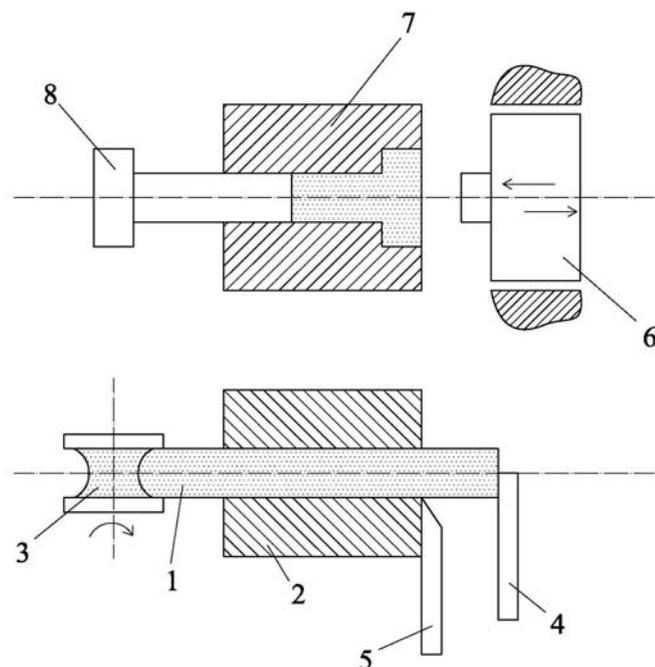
Схема высадки на холодновысадочном автомате: 1 – заготовка; 2 –отрезная матрица; 3 – роликовая подача; 4 – регулируемый упор; 5 – отрезной нож; 6 – высадочный пуансон; 7 – высадочная матрица; 8 – ползун
